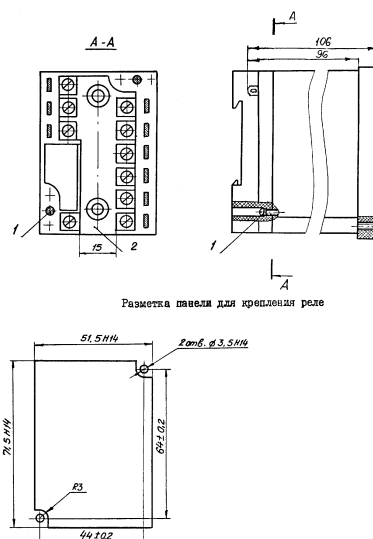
Габаритные, установочные, присоединительные размеры реле (утопленный монтаж):
